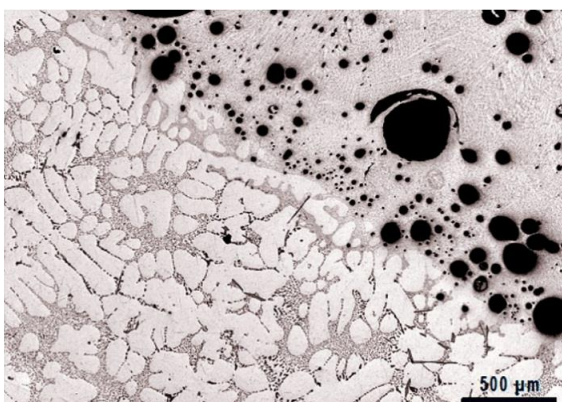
Газовые (водородные) поры при сварке алюминиевых сплавов
